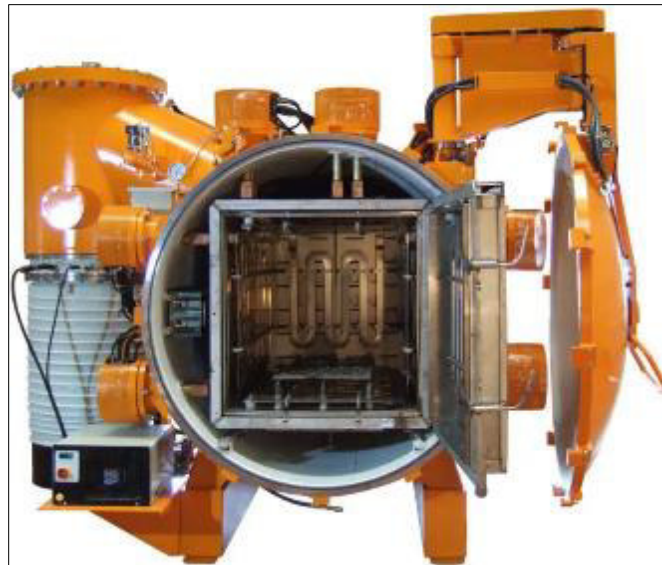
Horno de retorta para soldadura fuerte de aluminio.
